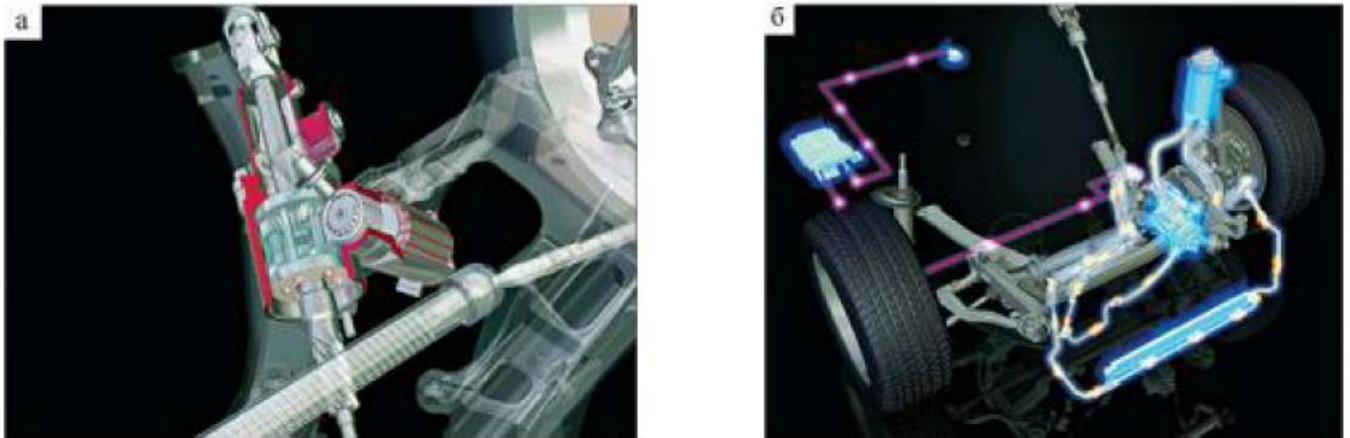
Система AFS: а – рульовий механізм; б – загальний вигляд.
